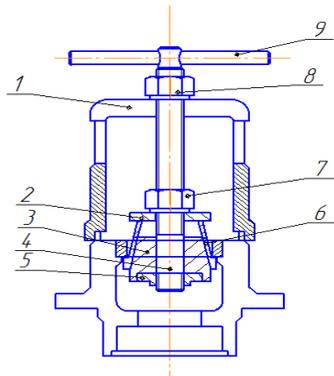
Съемник для выпрессовки обойм с помощью конуса и втулки
